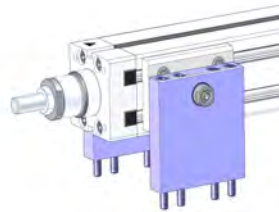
Lagebock für Schwenkzapfenbefestigung
